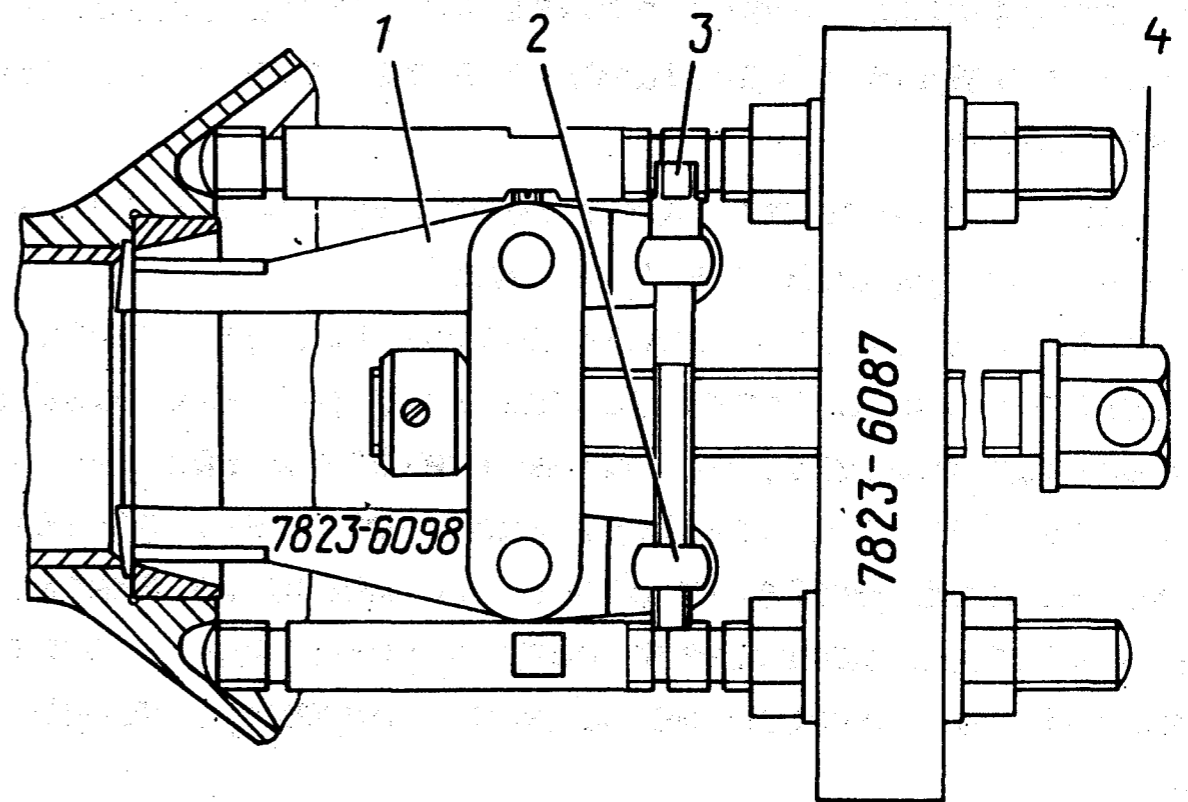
Выпрессовка наружного кольца подшипника коробки дифференциала из картера заднего моста: 1 - лапки съемника 7823-6098; 2 - ось; 3 - болт; 4 - винт
